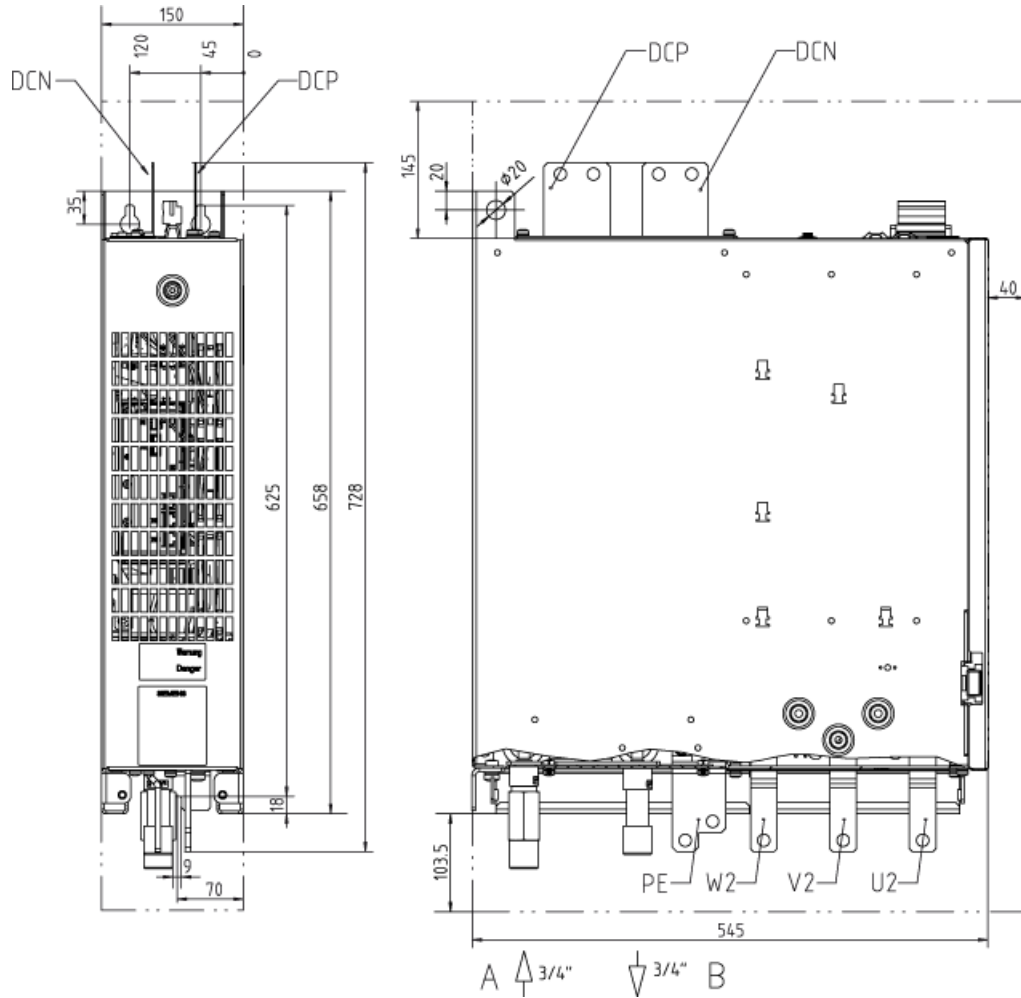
Габаритный чертёж модуля двигателя, типоразмер FXL. Вид спереди, вид сбоку
